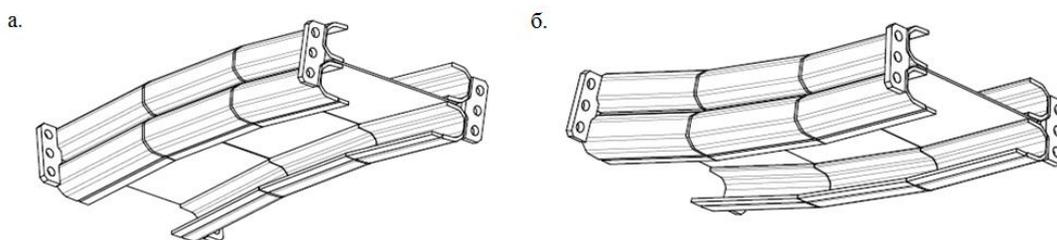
Поворотный неразборный рештак: а – верхний выпуклый, б – нижний вогнутый
